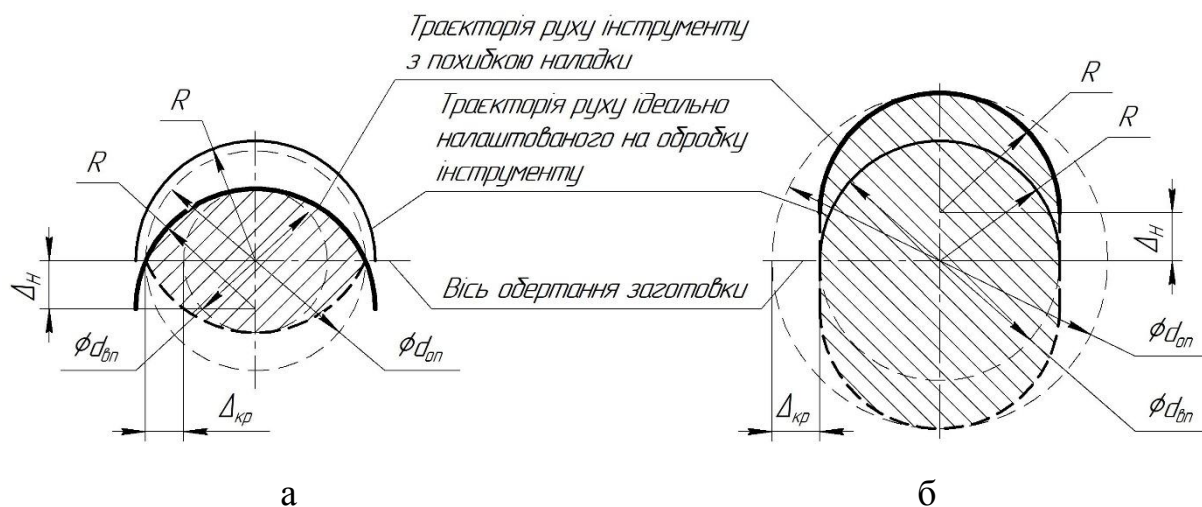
Спотворення форми деталі при радіальному зміщенні інструменту до (а) і від осі (б) обертання заготовки:
